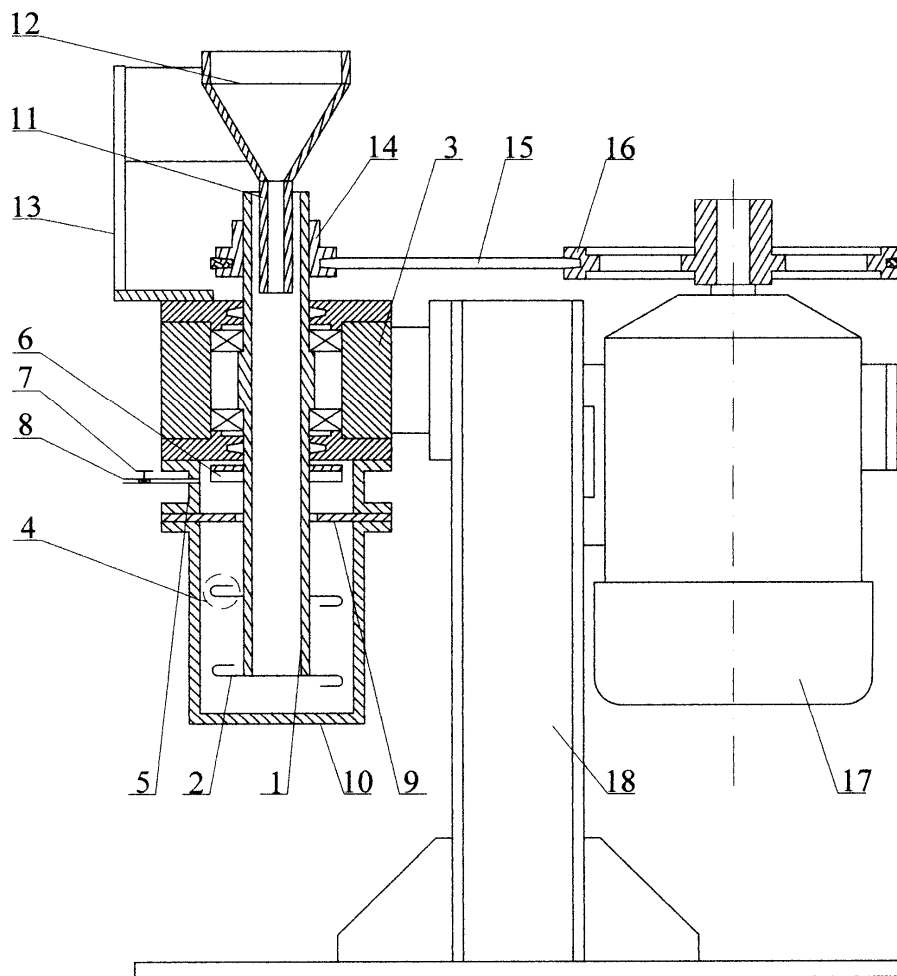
Схема лабораторного відцентрового млина: 1 – вал млина; 2 – робочий орган; 3 – корпус підшипникового вузла; 4 – корпус помольної камери; 5 – равликівий корпус; 6 – крильчатка; 7 – вентиль; 8 – вихідний патрубков; 9 – диск; 10 – корпус помольної камери; 11 – завантажувальна воронка; 12 – верхній рівень завантажувальної воронки; 13 – стойка для воронки; 14 – шків млина; 15 – ремінь; 16 – шків двигуна; 17 – двигун; 18 – опорна стойка.
